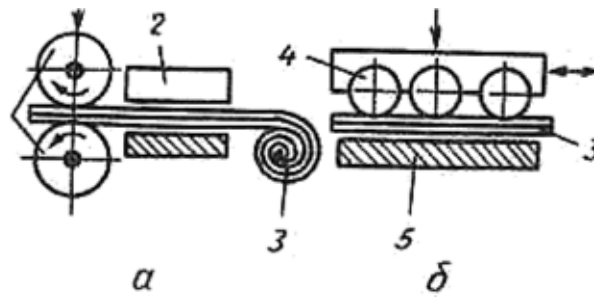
Схема получения сварного шва с помощью ролика под действием температуры: 1 — ролики, предназначенные для продвижения материала; 2 — нагревательный прибор; 3 — сваривающая плёнка; 4 — передвижная каретка на нагревательных роликах; 5-поверхность, на которую ставится плёнка
